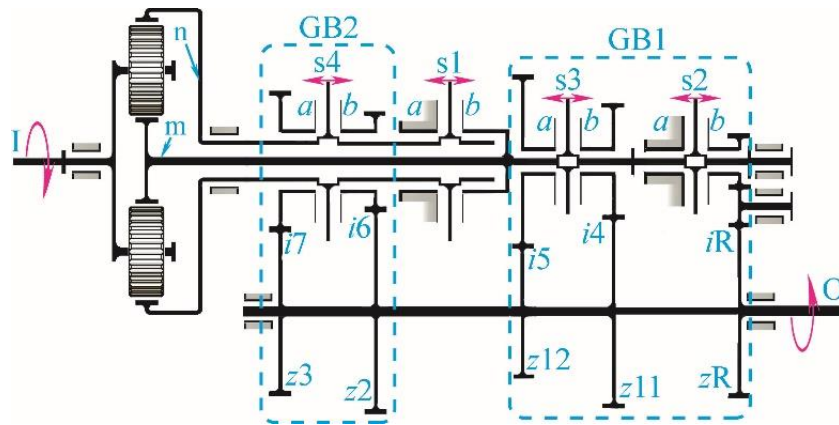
Кинематическая схема 12-ти ступенчатой двухшочной коробки DO.
